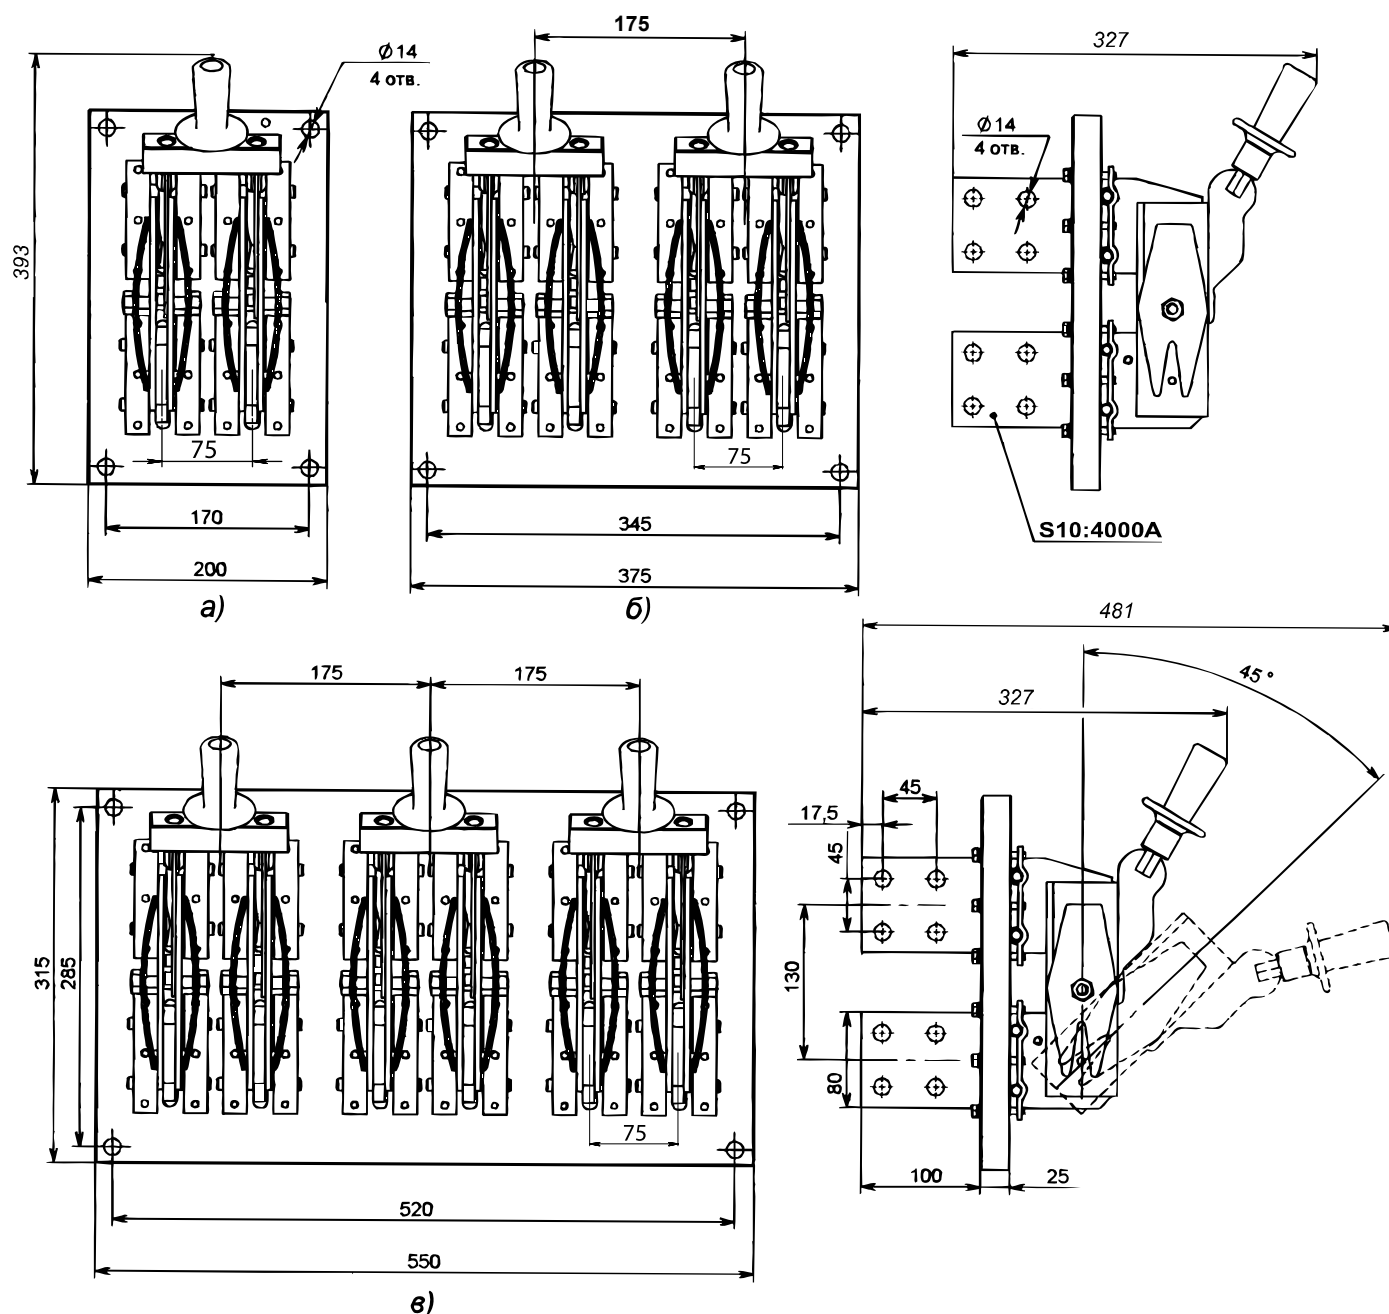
Разъединитель PE19 с центральным рычагом для управления штангой
